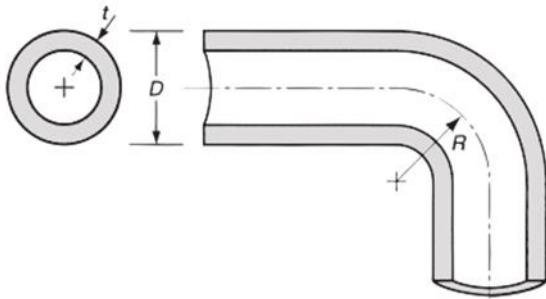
Dimensiones de doblado de láminas tubulares (Groover, 2007).
